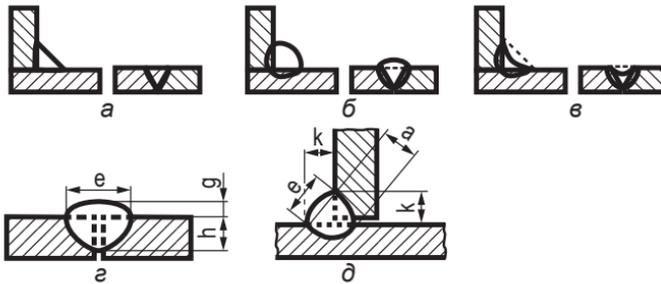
Виды сварных швов (*a* — плоский; *б* — выпуклый; *в* — вогнутый) и характеристики стыкового (*з*) и углового (*д*) швов: *e* — ширина шва; *h* — глубина проплавления; *g* — выпуклость (усиление) шва; *a* — толщина шва; *k* — катет шва
